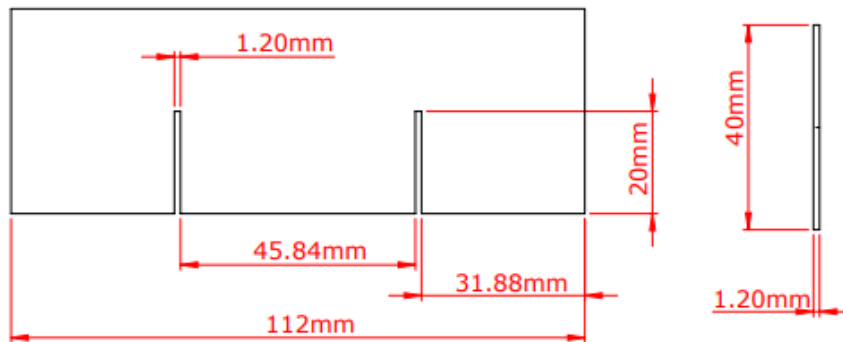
Sección 2 de la cuchilla circular - Detalle de las dimensiones
